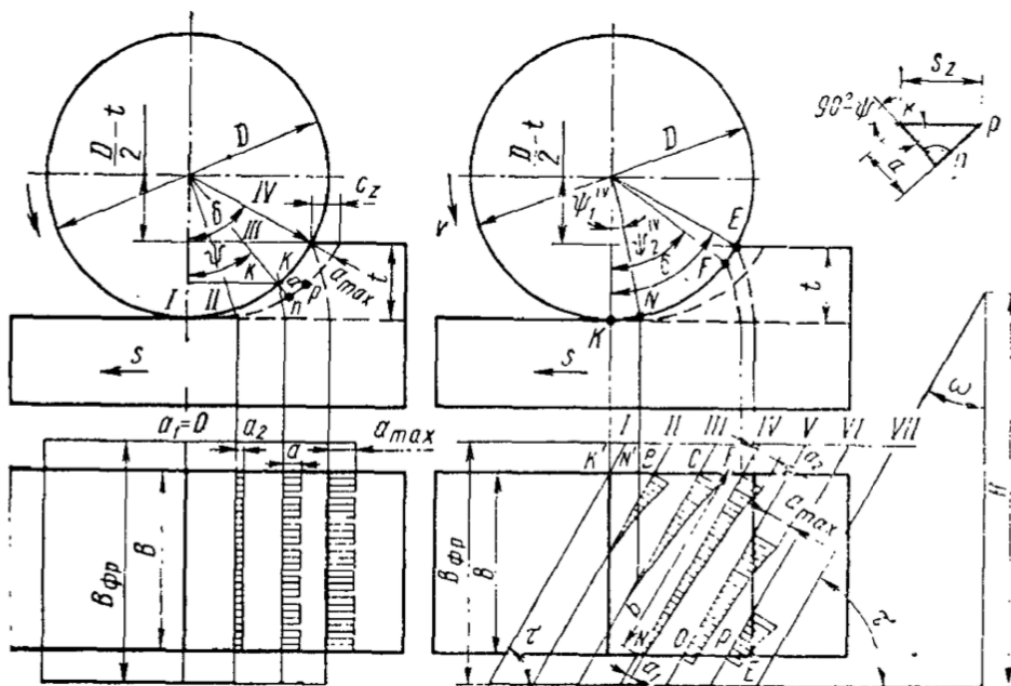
Елементи різання при роботі циліндричною фрезою:
